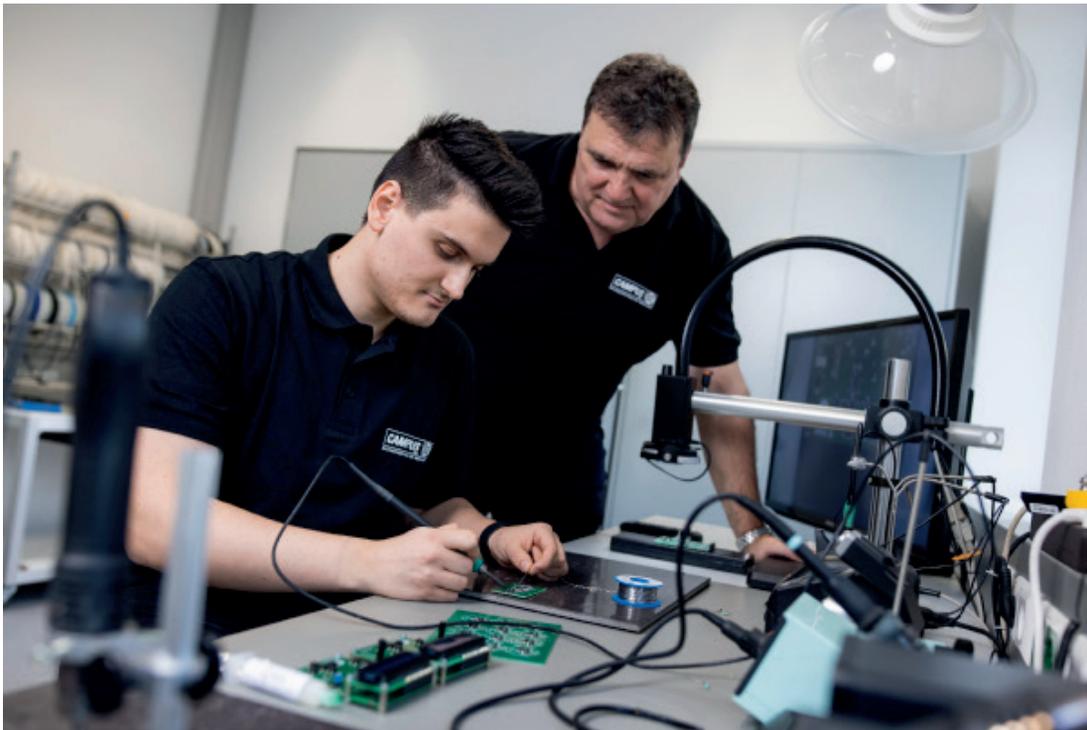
Bearbeitung von Prototypen-Leiterplatten im Electronic Engineering and Assembly Lab.
